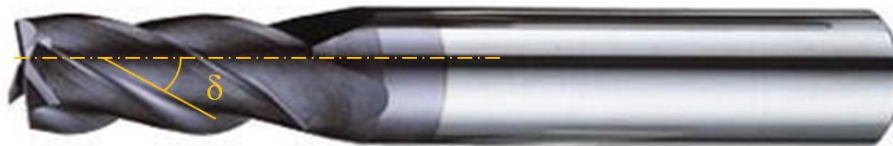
Ângulo de hélice (δ) em fresas frontais integrais de topo [Dormer Tools, 2015].
